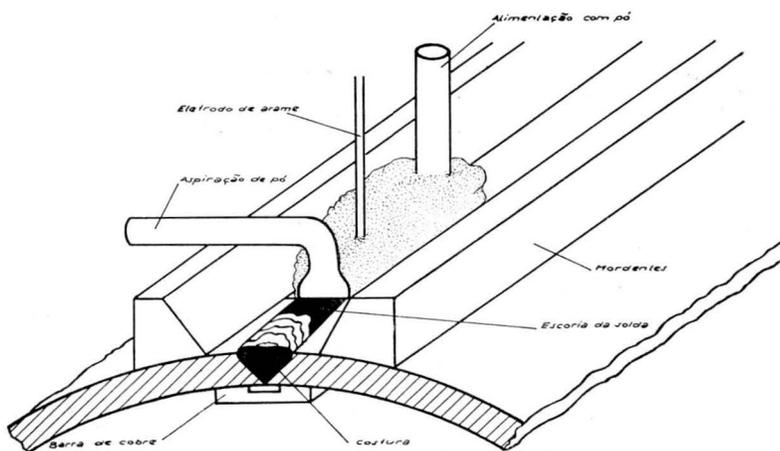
Solda sob pó protetor, sistema «ELLIRA».
